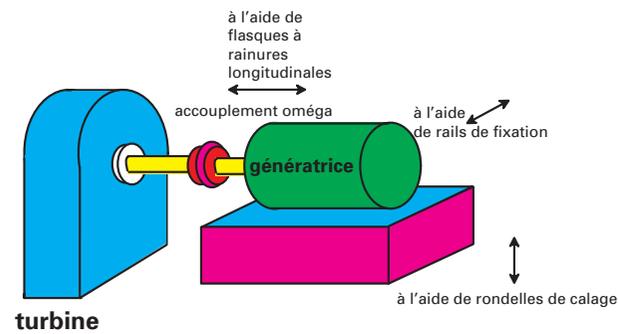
Exemple de configuration de montage permettant l'alignement précis des axes des deux machines
